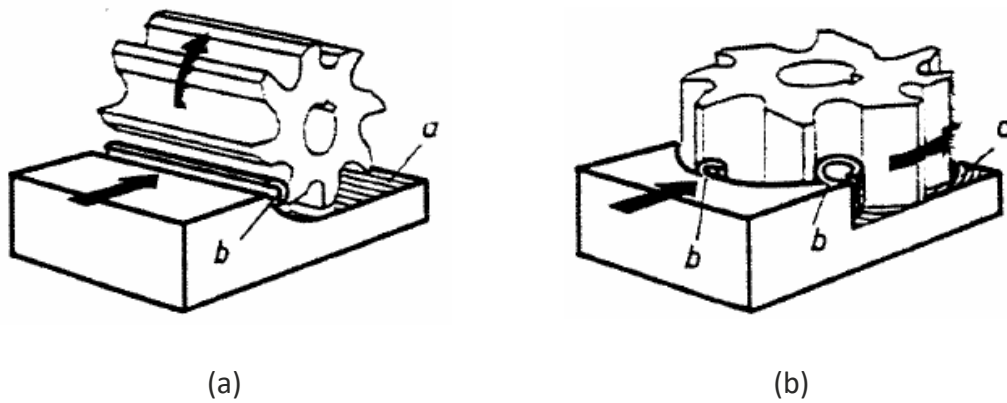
Fresagem a) cilíndrica, b) frontal ou de topo (Gerling, 1977)
